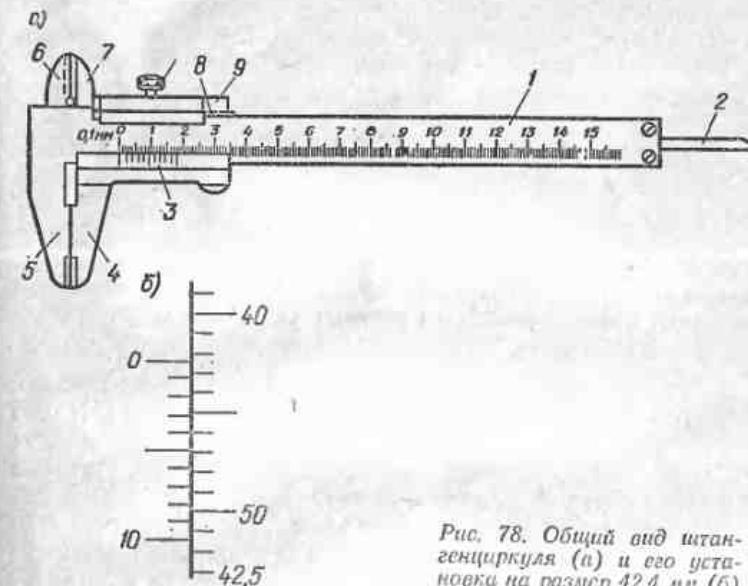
Общий вид штангенциркуля (а) и его установка на размер 42,4 мм (б)
